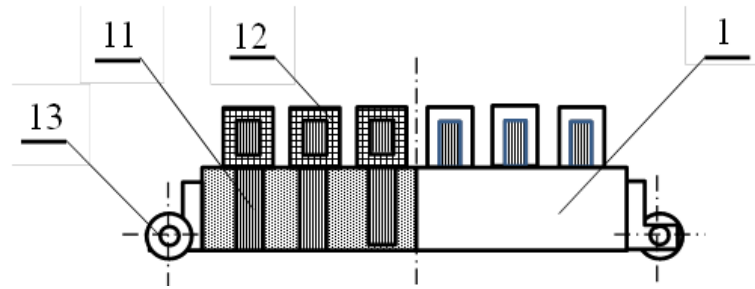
Індукторний поворотний модуль зі змінною геометрією активної поверхні.
